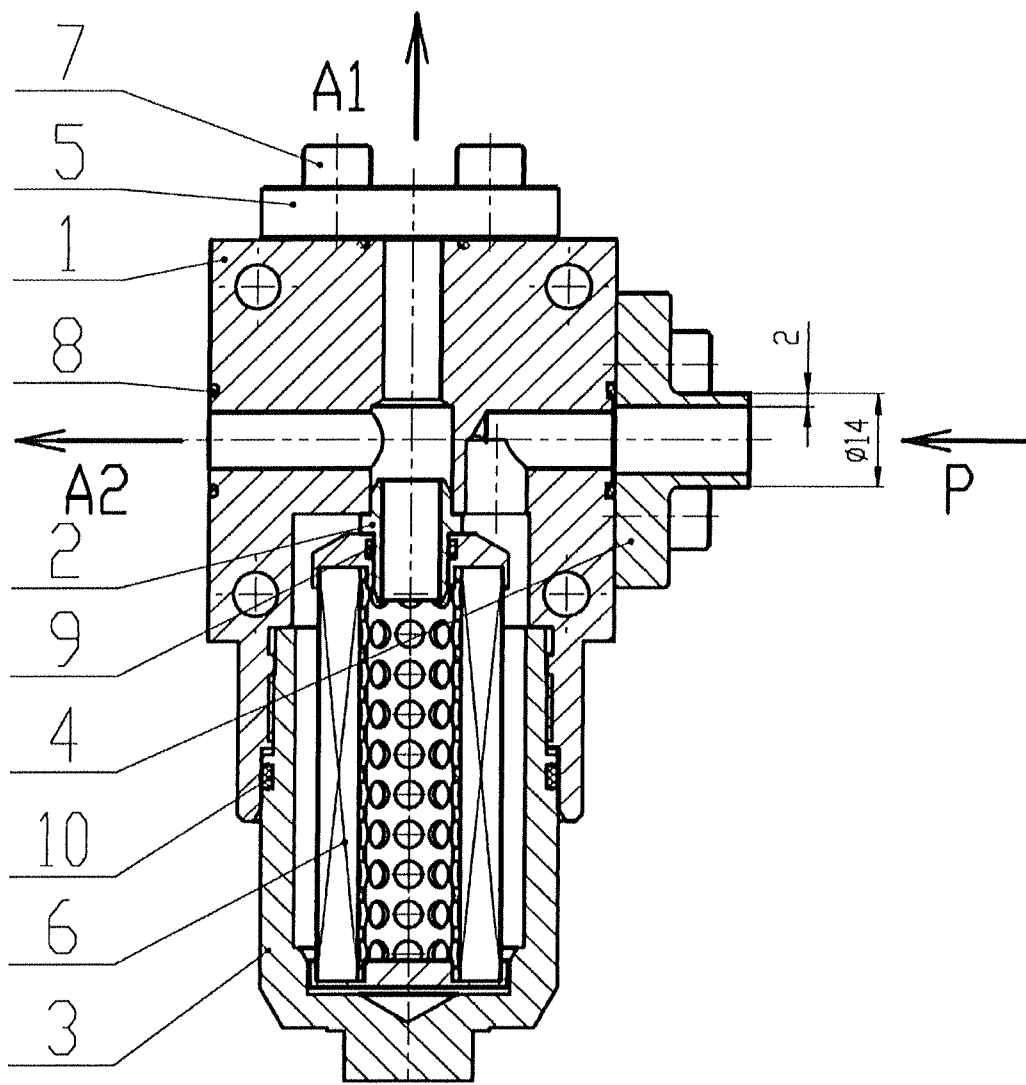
Габаритные, присоединительные размеры конструктивное исполнение и принципиальная схема фильтра Y70 117- 050 - DN10
